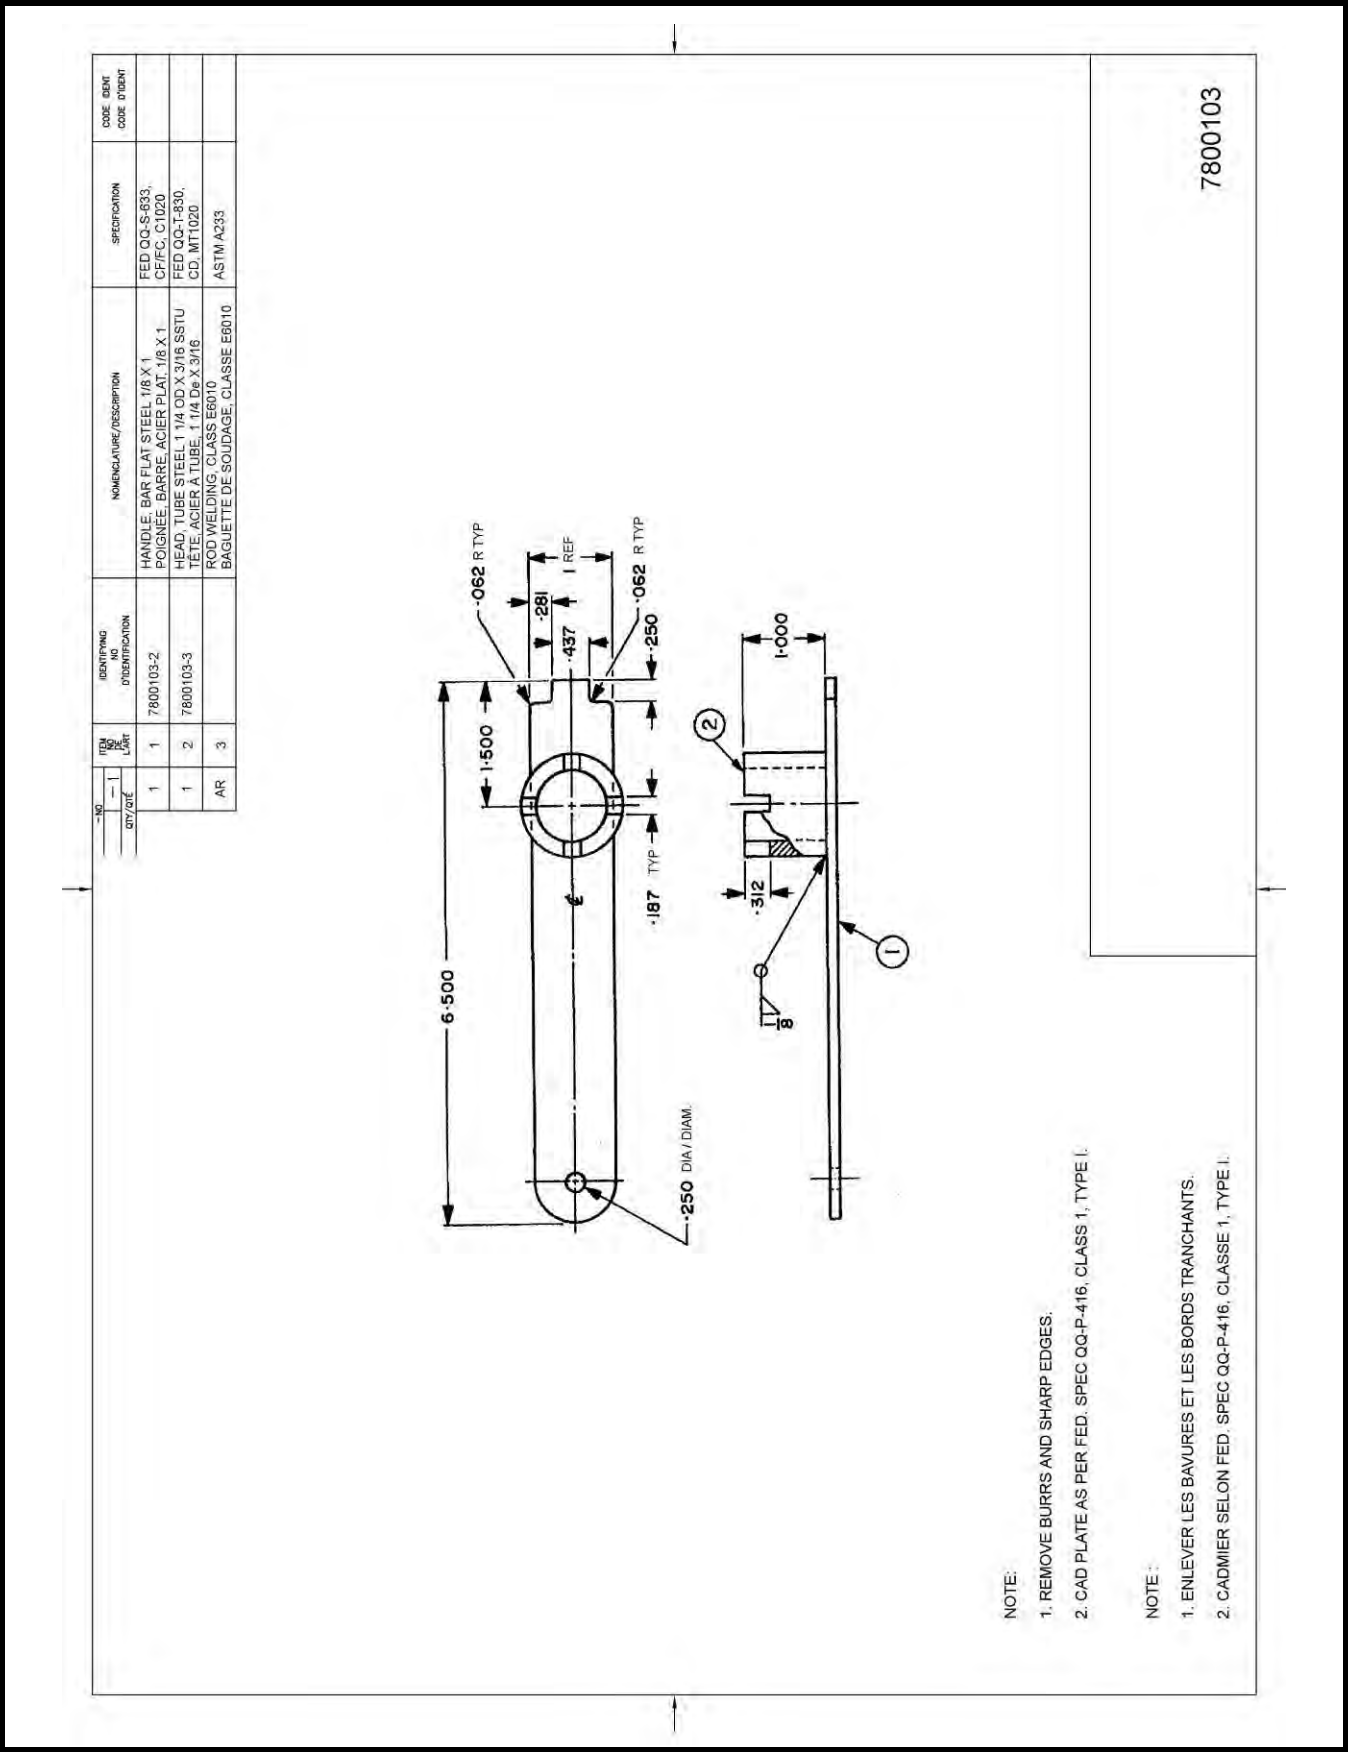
(feuille 2 de 2) Dessin d'ensemble inséparable
